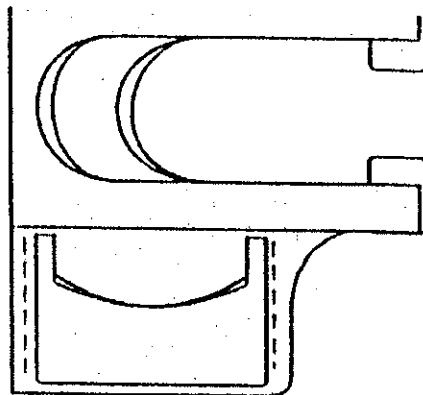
Контроль сварного соединения кронштейна поводка с опорной плитой
